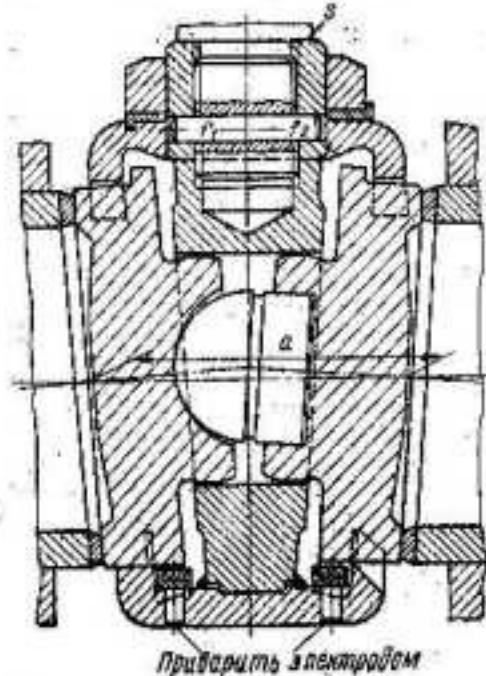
Самоустанавливающийся клиновой затвор задвижки.
